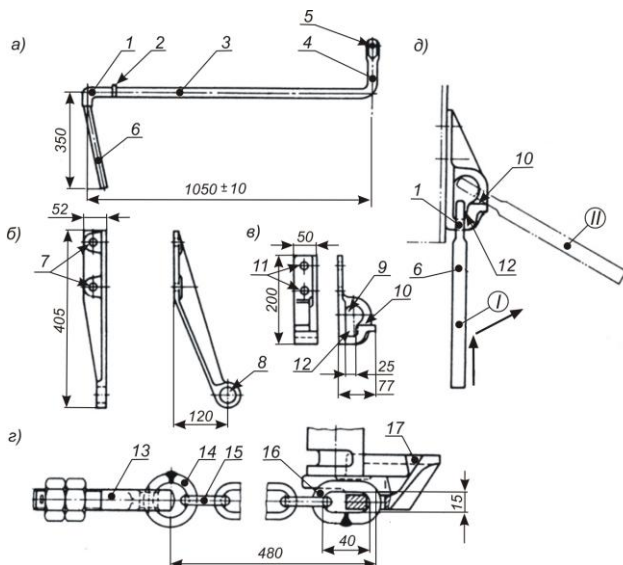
Детали расцепного привода и положения рукоятки рычага:
